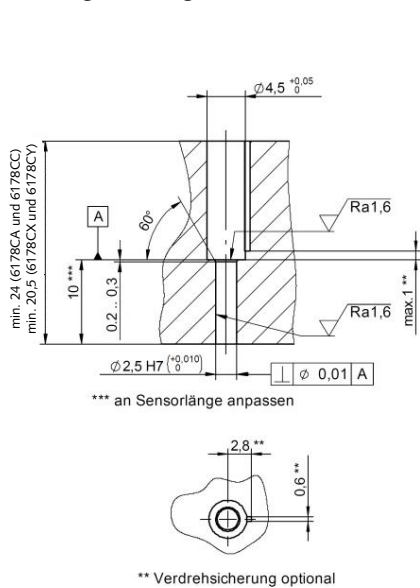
Montagebohrung für Einbau mit Distanzhülse
